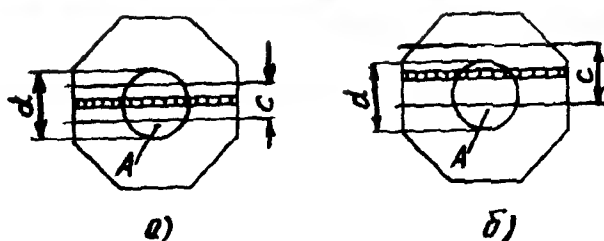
Выбор места для измерения толщины образца со сварным швом до и после испытания
